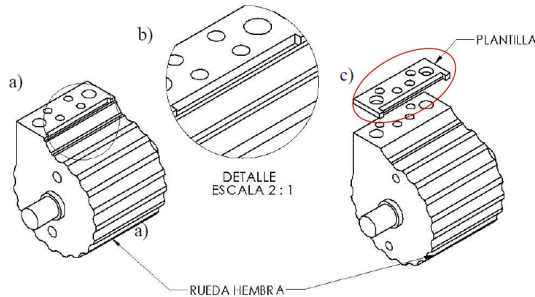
Pieza base estampador de unión DO: a) Pieza, b) Detalle
